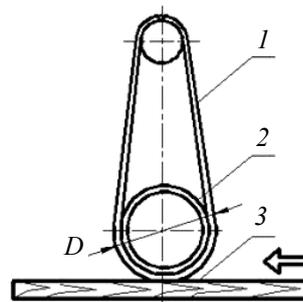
Широколенточный шлифовальный станок с верхним расположением агрегата:
